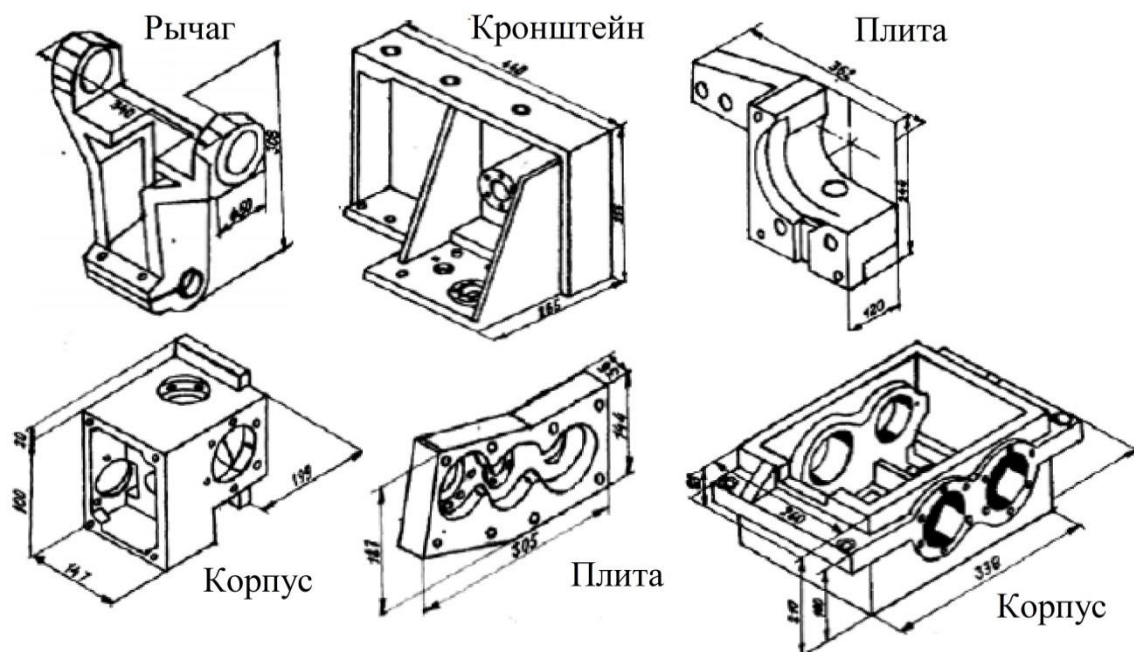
Детали-представители корпусных деталей для обработки на станках ГПС
